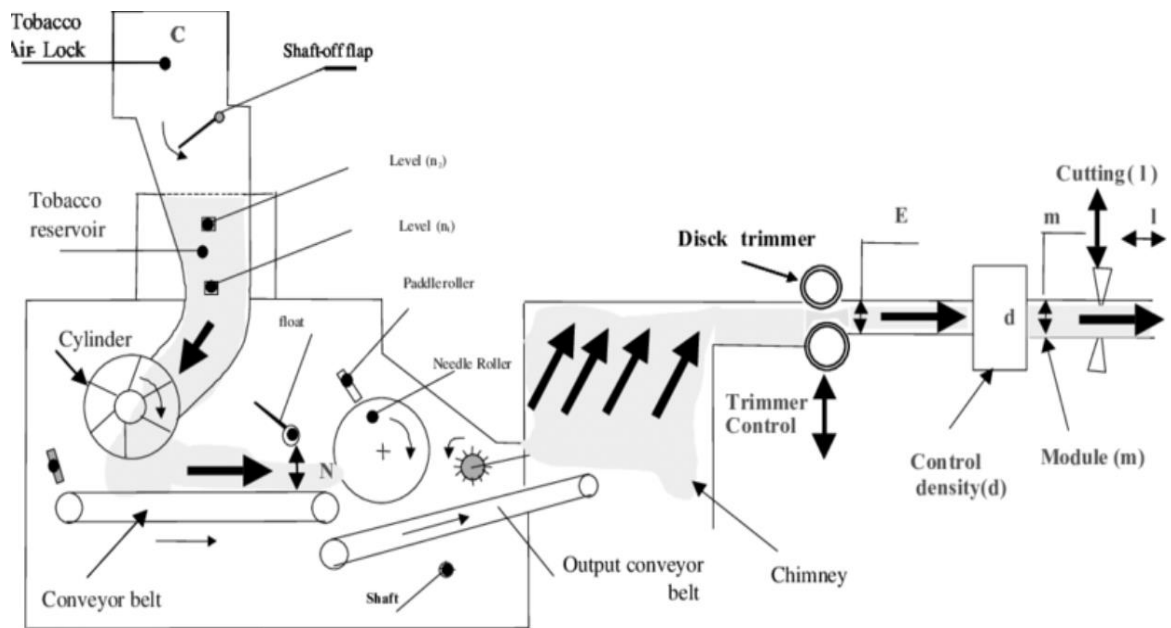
Схема формування і обрізки тютюнового шару
